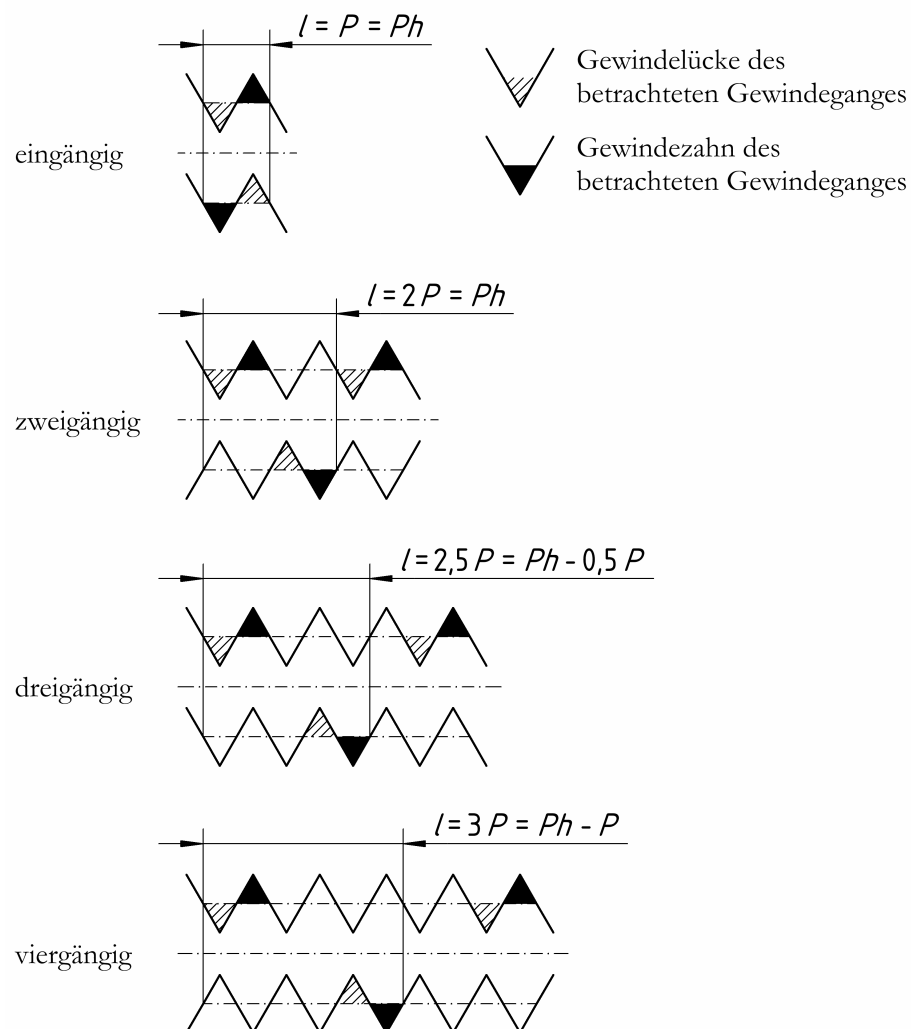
Bezugslängen des Flankendurchmessers ein- bis viergängiger Außengewinde
